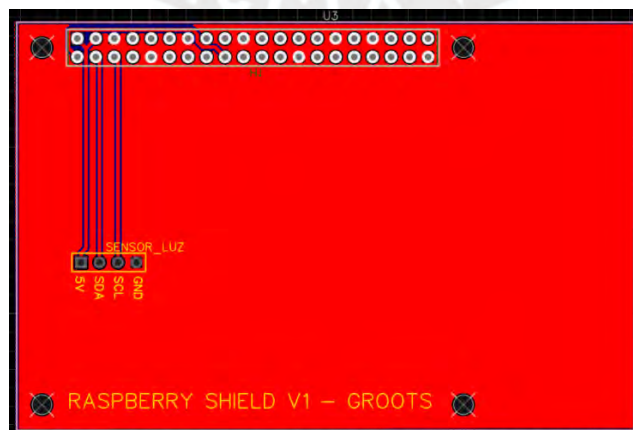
PCB diseñada. Fuente: elaboración propia.
